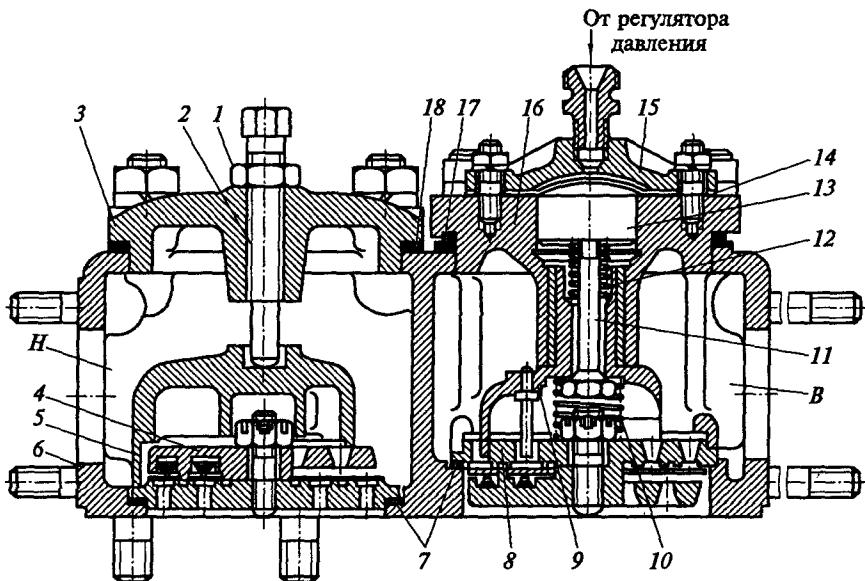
Клапанная коробка компрессора КТ-6:
